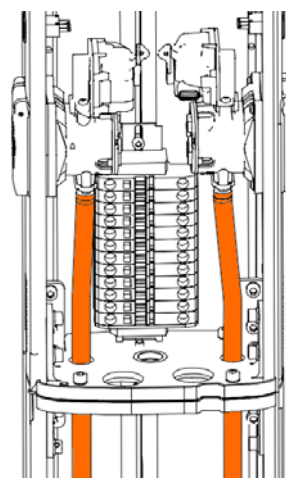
Montage Wasserablauf bei 2 Ladesteckern
